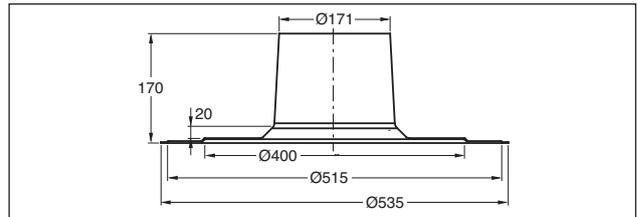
Flachdach-Klebeflansch (Maße in mm)
